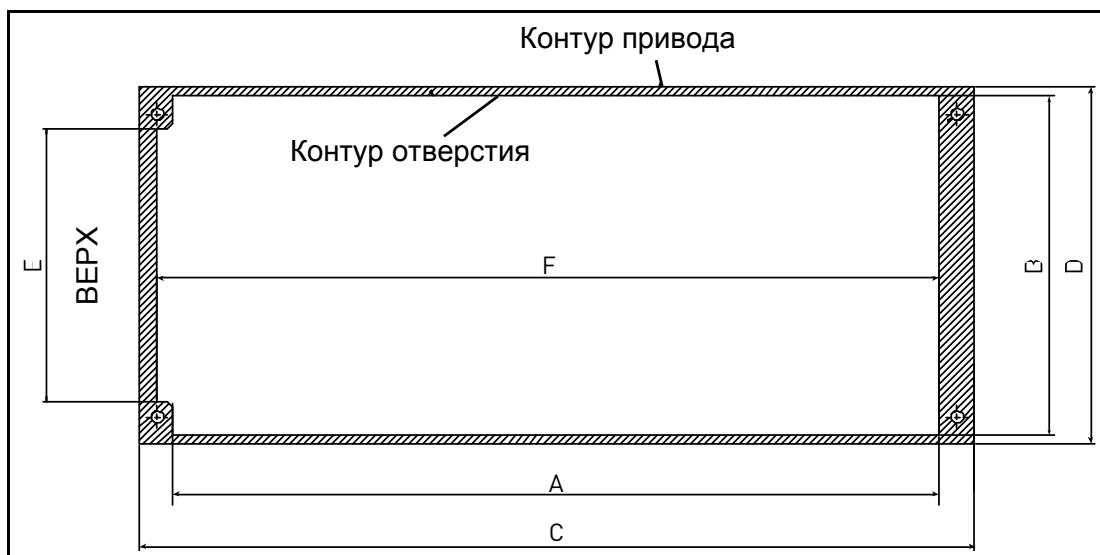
Размеры выреза для утопленного монтажа приводов типоразмеров MR4–MR6
